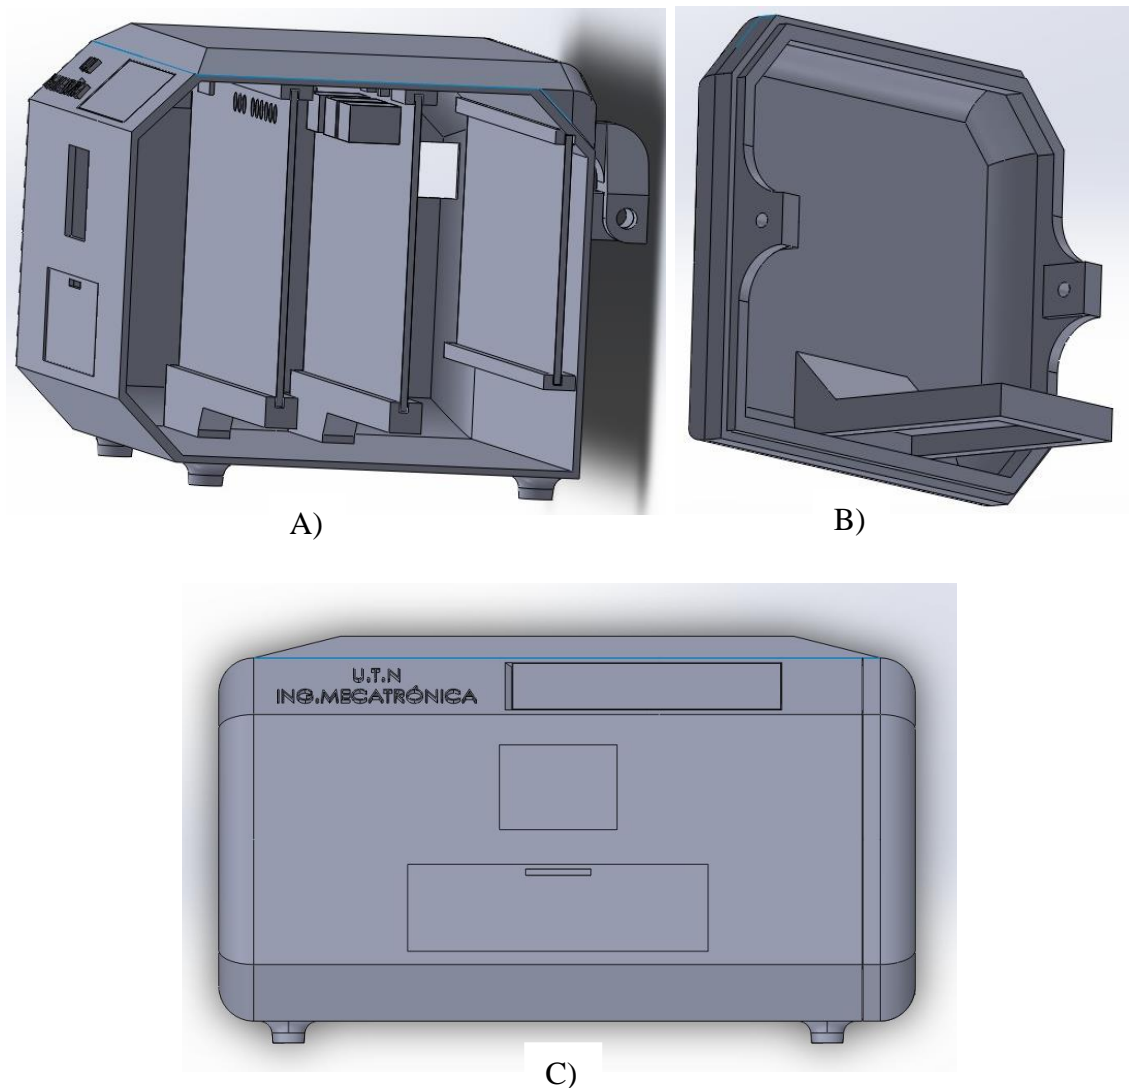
A) Pieza 1 soporte principal, B) Pieza 2 tapa del soporte, C) Ensamblaje de la estructura.
